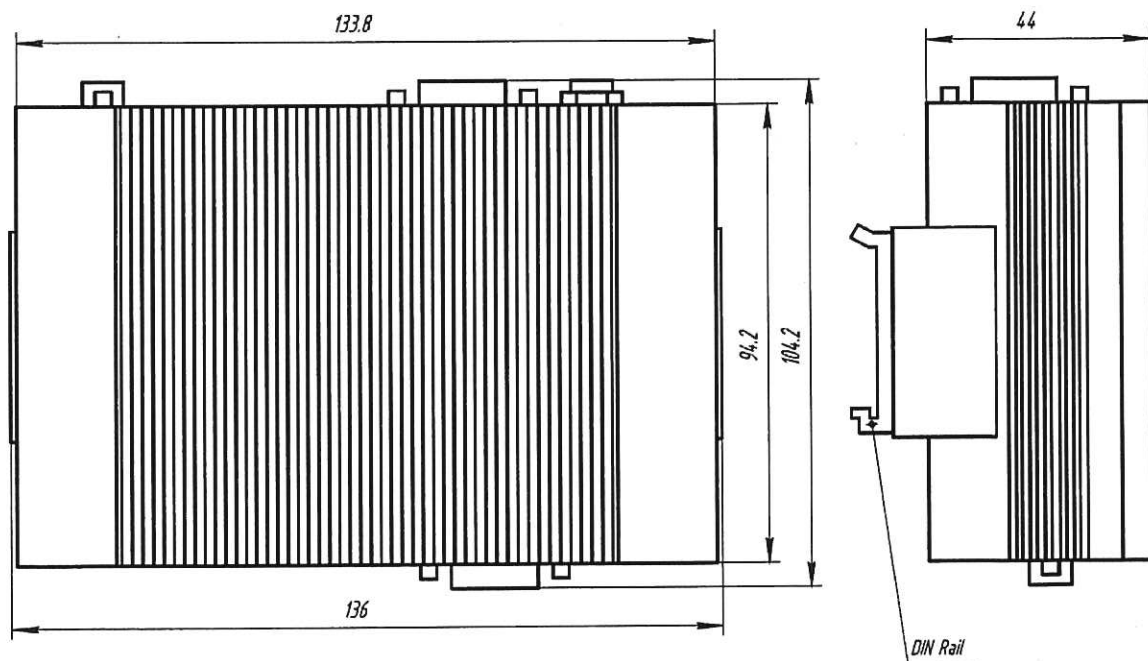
Внешний вид и габариты PCE-P-02-NRW (виды сверху и сбоку).
